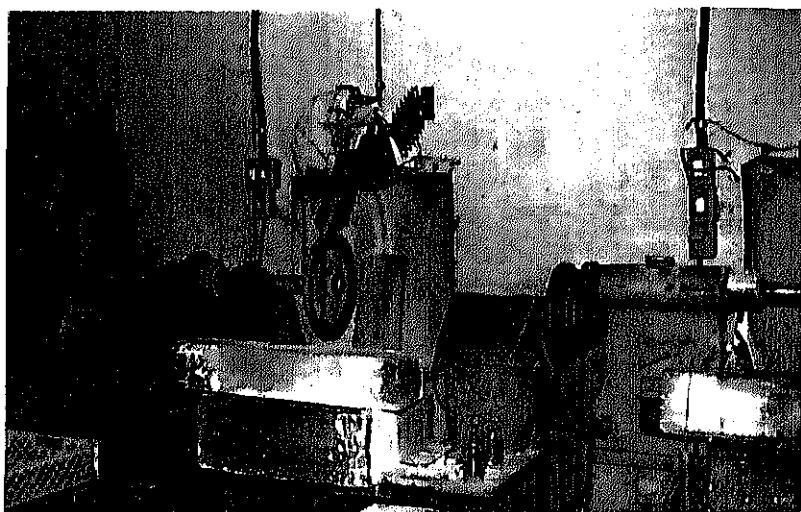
Rueda de corcho sobre motor eléctrico utilizada para abrillantar y pulir.
